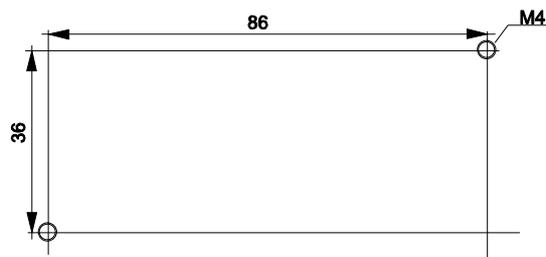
zeigt den Bohrplan zur Befestigung des Gerätes
